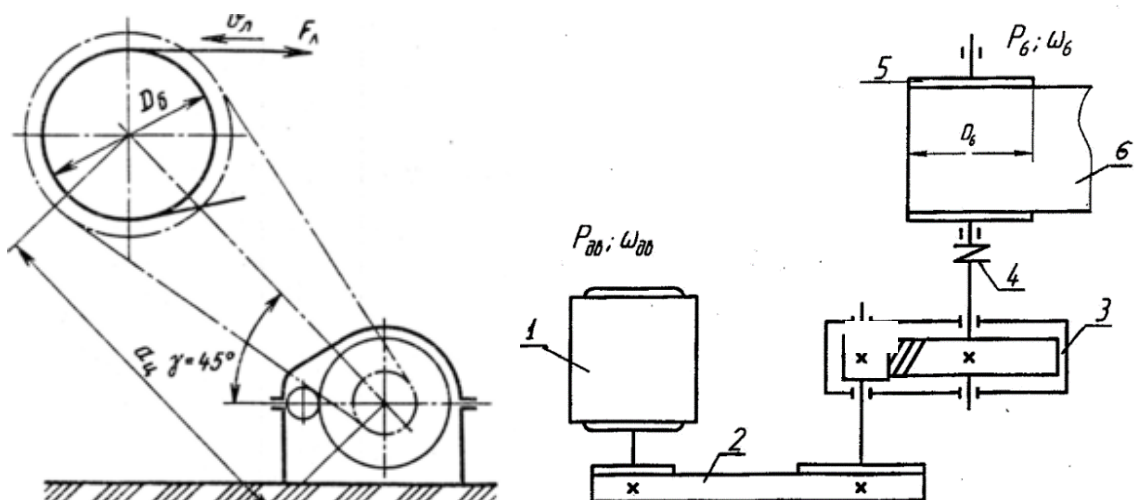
Привод ленточного конвейера с цилиндрическим редуктором и клиноремённой передачей: 1- электродвигатель; 2 - клиноремённая передача; 3 - одноступенчатый цилиндрический редуктор; 4 - муфта; 5 - приводной барабан; 6 – лента конвейерная.
